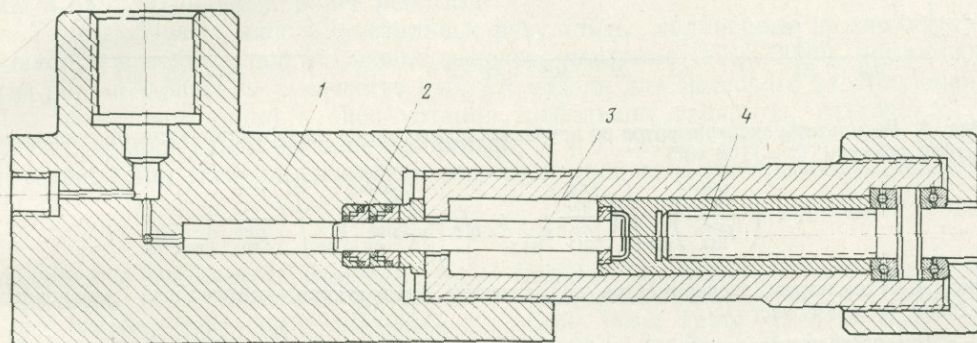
Ручной пресс для давлений до 5000 кг/см²
